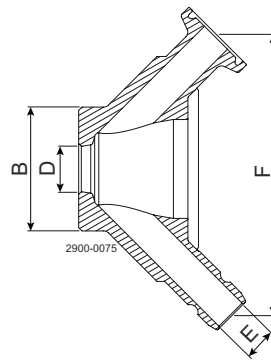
Ventilgehäuse: Tankschweißen
